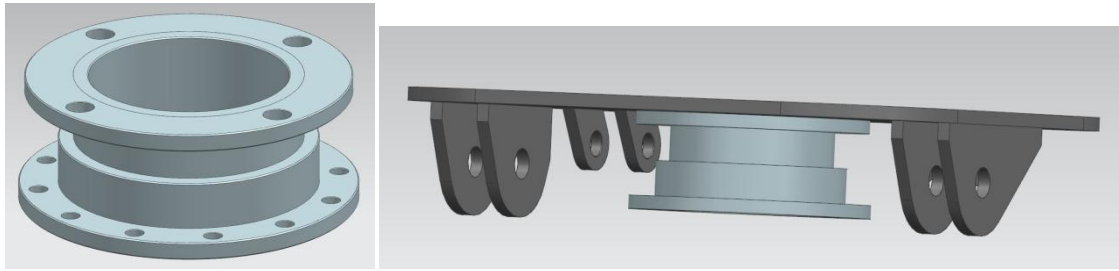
38. A la dreta el suport del motor, a l'esquerra l'assemblatge amb la taula.
